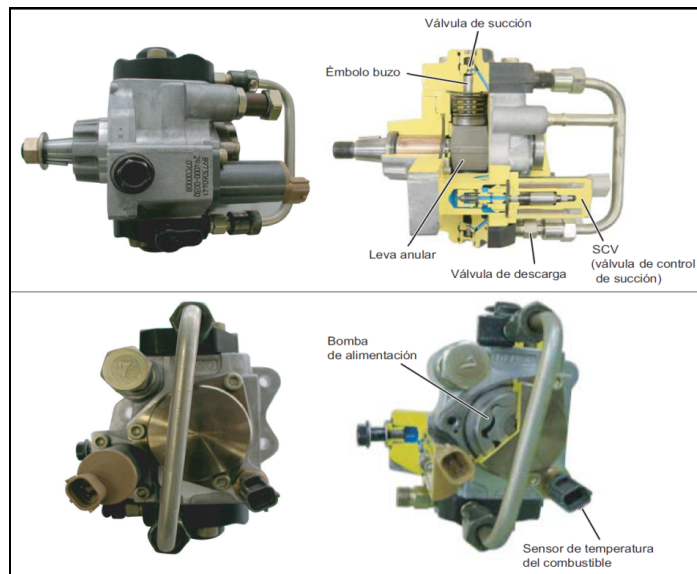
Partes de la bomba de suministro - alta presión HP3.
